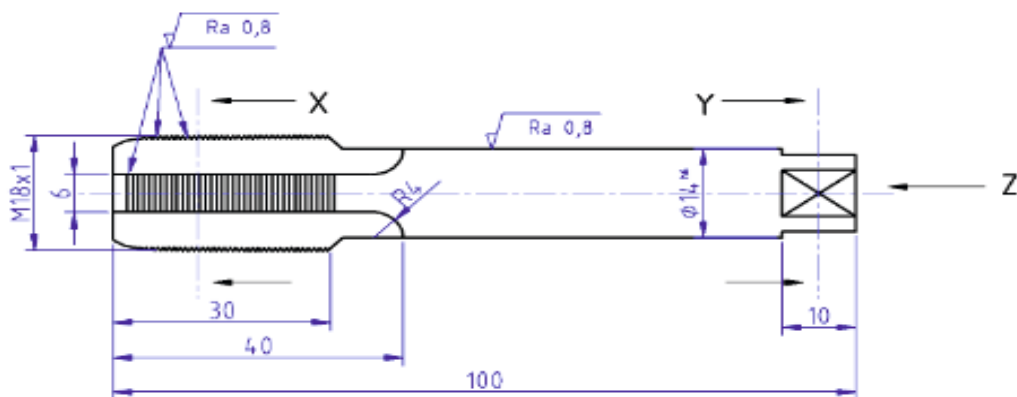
Zeichnungsausschnitt Gewindebohrer (Quelle: Jakob-Preh-Schule)
